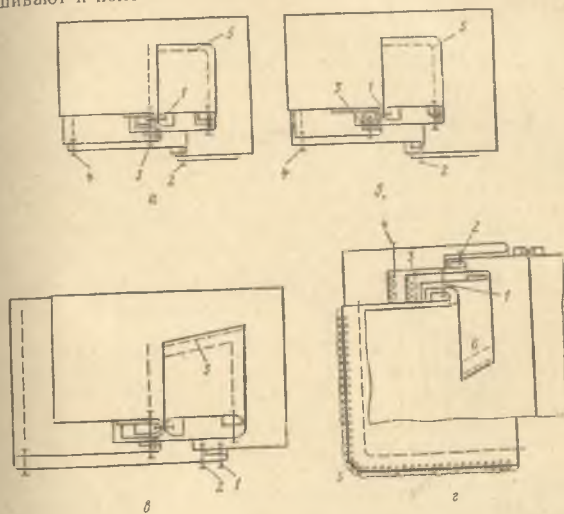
Сборочные схемы бокового прорезного кармана с листочкой
